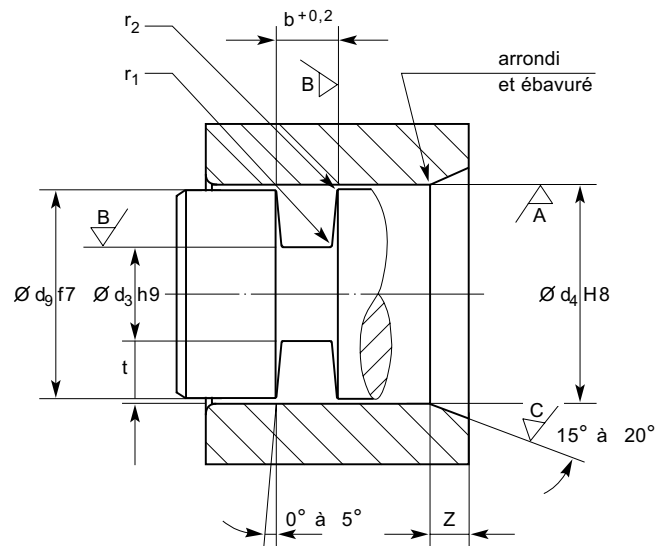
Joint de piston – hydraulique et pneumatique
